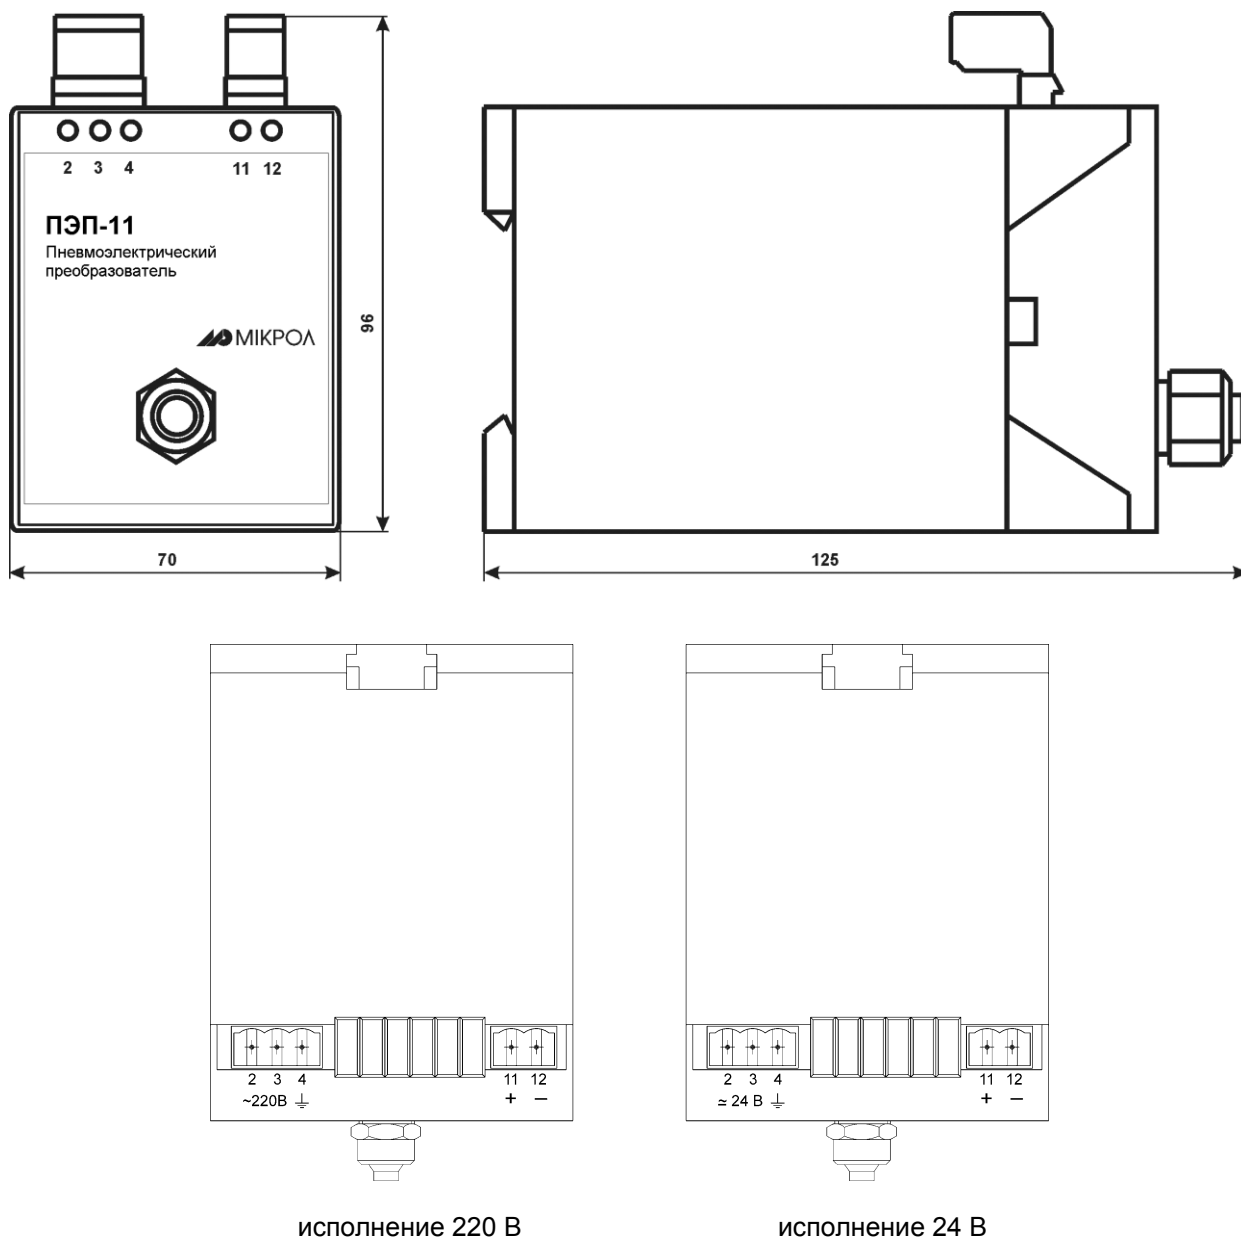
Внешний вид и габаритные размеры ПЭП-11(преобразователь давления)
